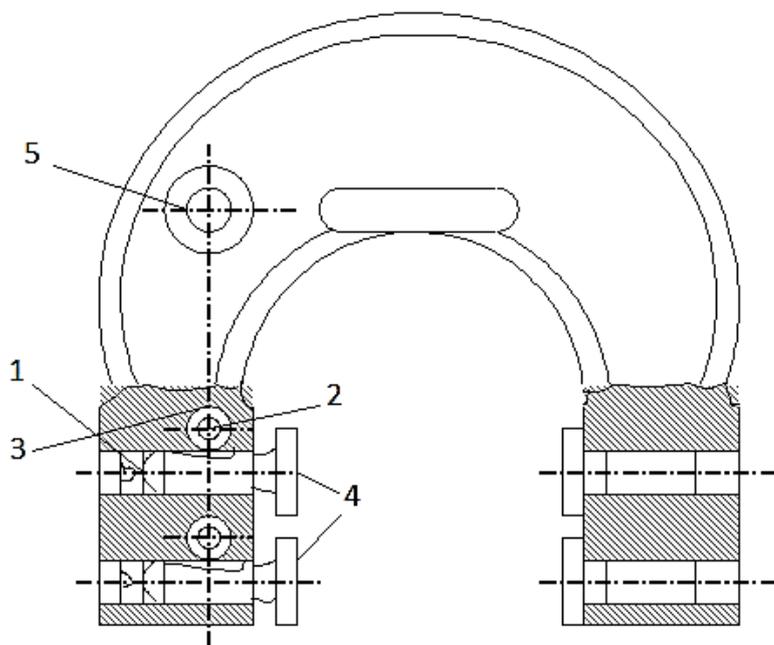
Регулируемая калибр-скоба: 1 – установочный винт; 2 - затяжной винт; 3 – затяжная втулка; 4 – вставка; 5 - маркировочная шайба.
